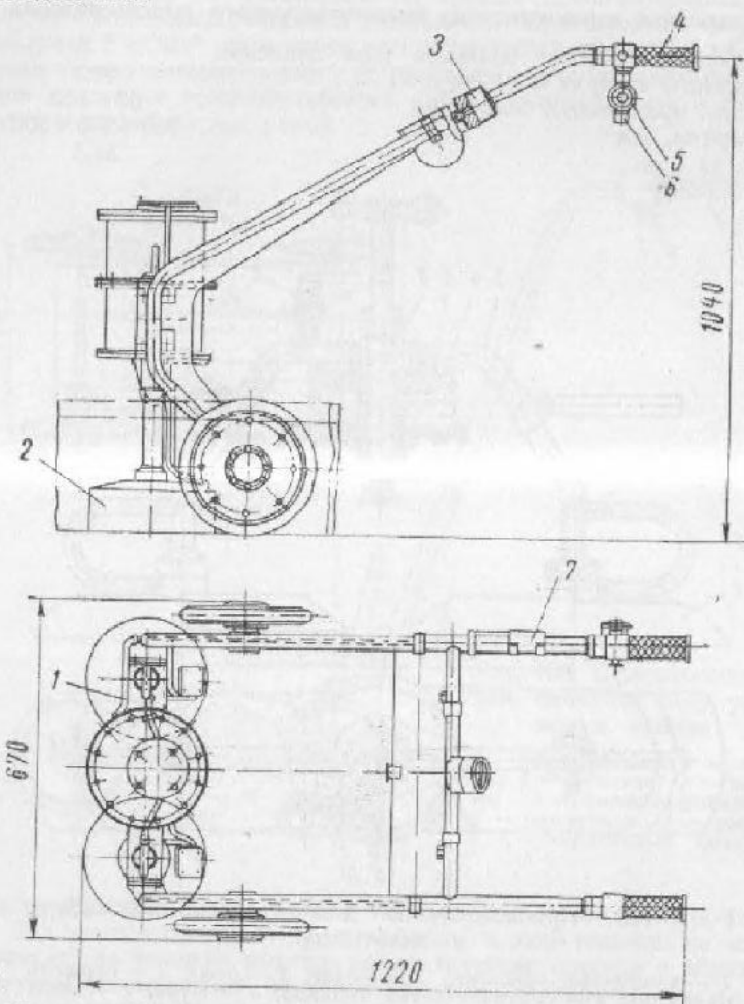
Пневмоманнитное приспособление для прижима-ния набора к полотнищу.
